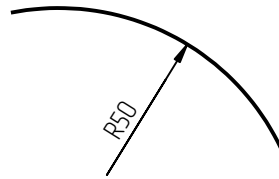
Размерную линию допускается *не доводить* до центра дуги (обрывать)
